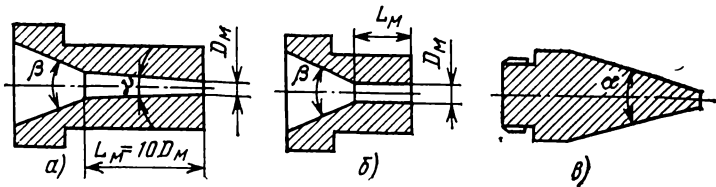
Формующий инструмент для изготовления корделя из полиэтилена для радиочастотных кабелей.
